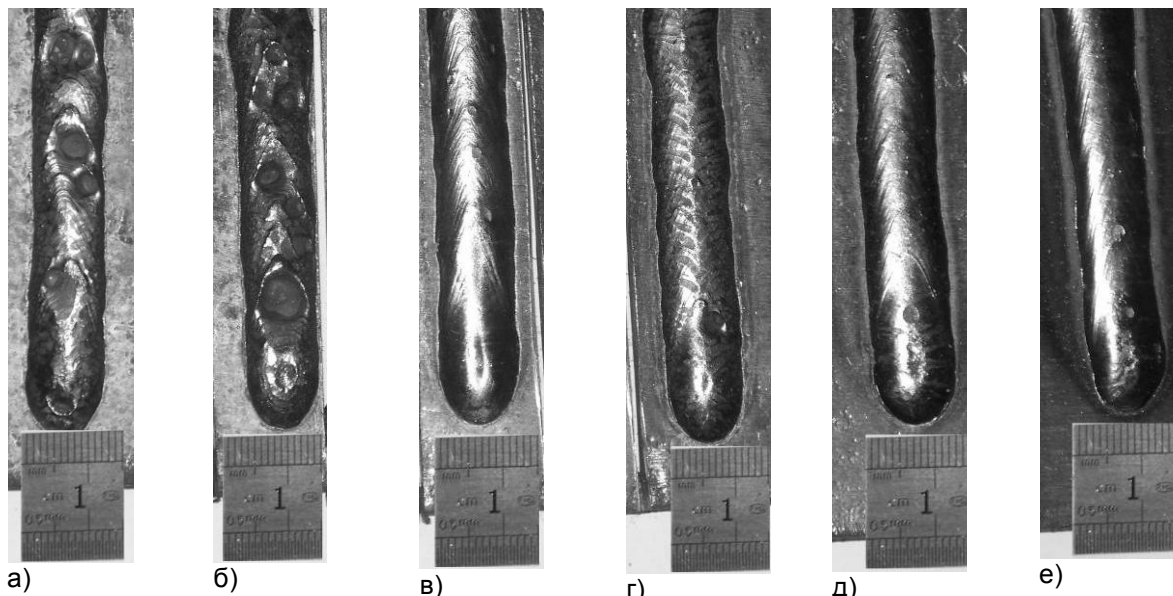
Валики, наплавленные автоматической сваркой под слоем флюса АН-47 испытательных проб: а) – I, б) – II, в) – III, г) – IV, д) – V, е) – VI
